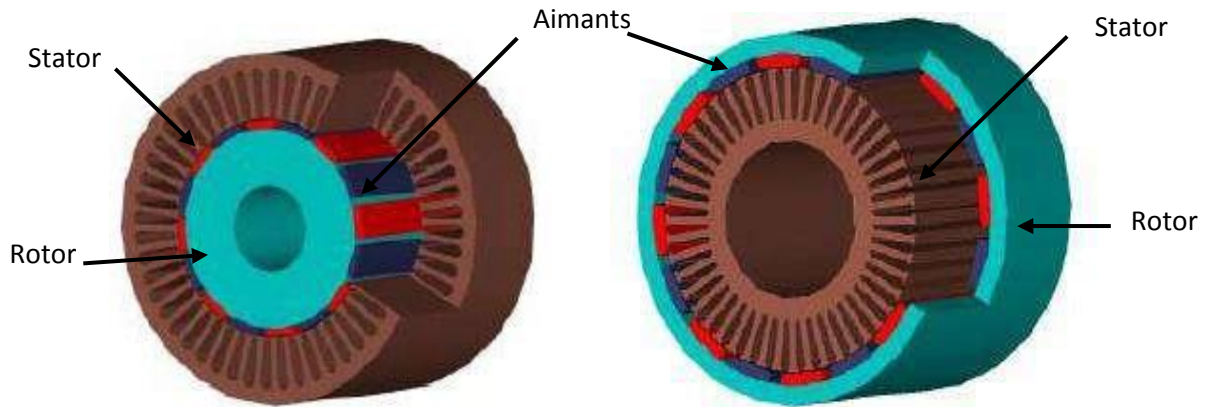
Exemple de structures à rotor interne et à rotor externe.
